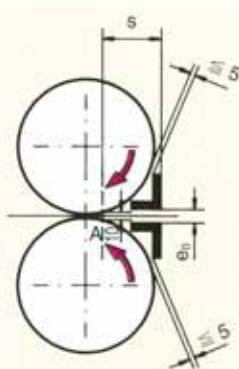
Barres de protection et profilés de protection placés aux zones d'entraînement.
